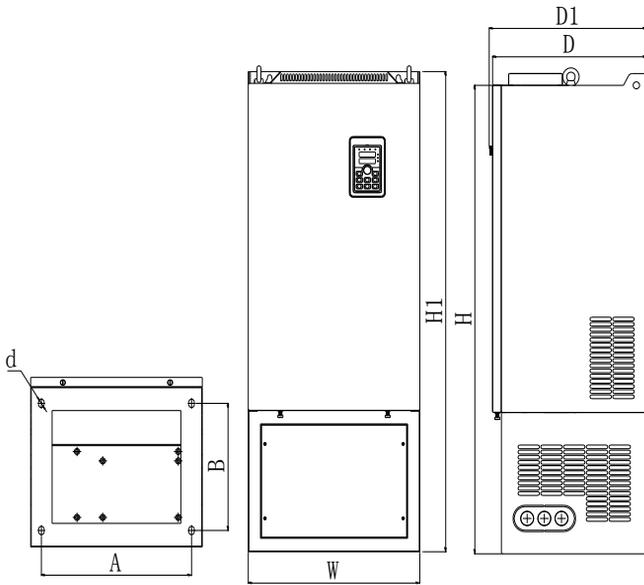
132kW G3 (带有直流电抗器底座)外形尺寸
